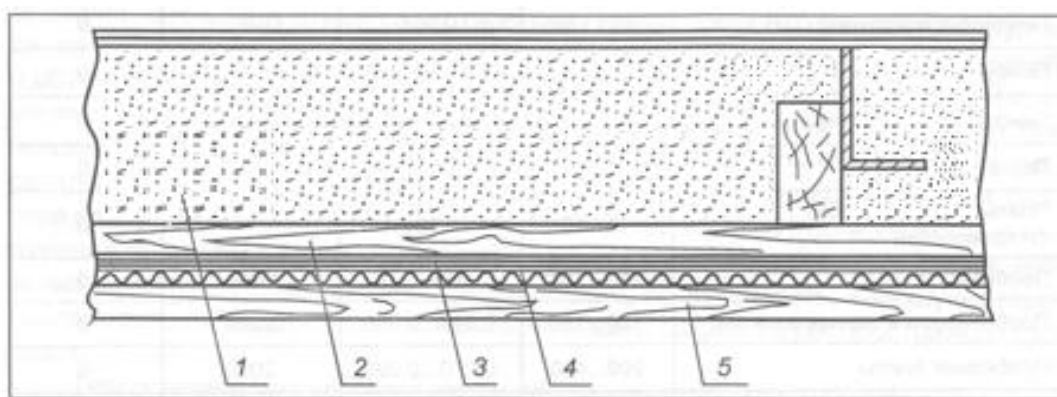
Нормальная судовая изоляция: 1 – тепловая изоляция, 2 – первый слой досок, 3 – пароизоляция, 4 – сетка, 5 – второй слой досок
